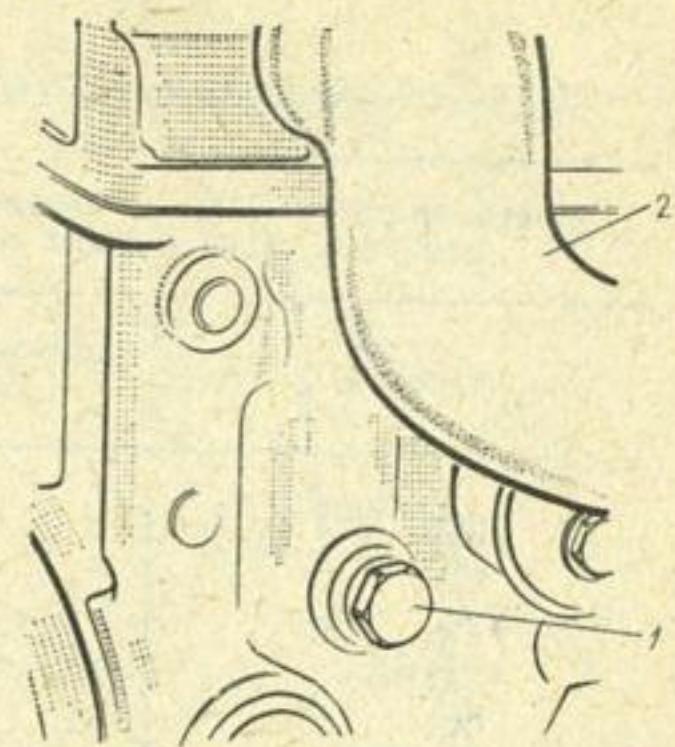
Пробка сливного отверстия на стенке рубашки охлаждения блока цилиндров:
